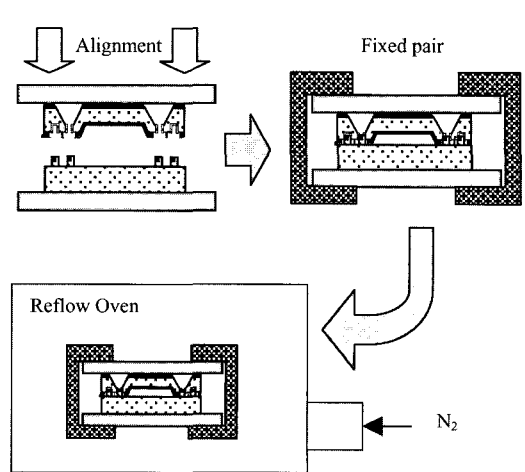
웨이퍼 레벨 정렬 및 리프로우 접합 (“LEGO-like assembly”)
